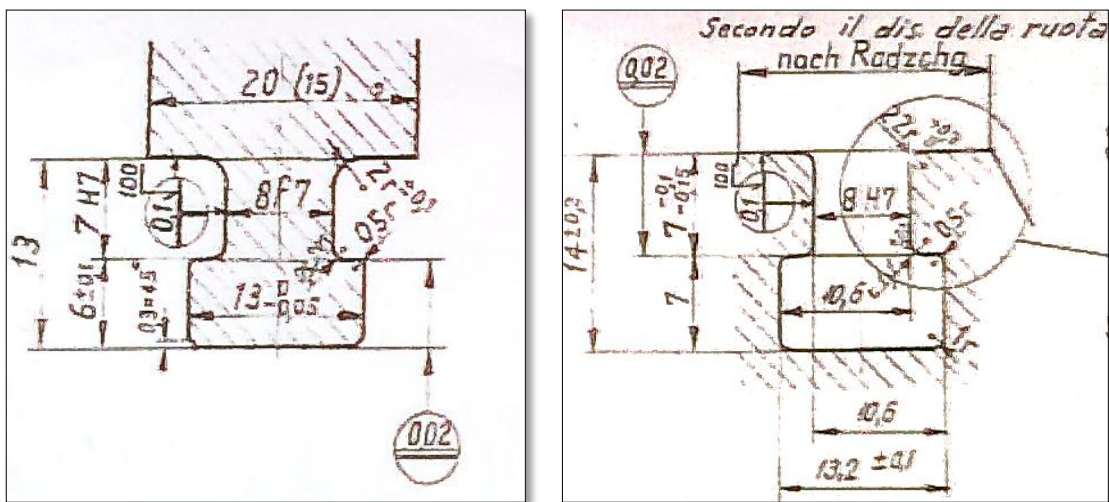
dimensioni del piede palare (a sinistra) e della cava (a destra) sul disco del 2° e 5° stadio della macchina n° 1.
